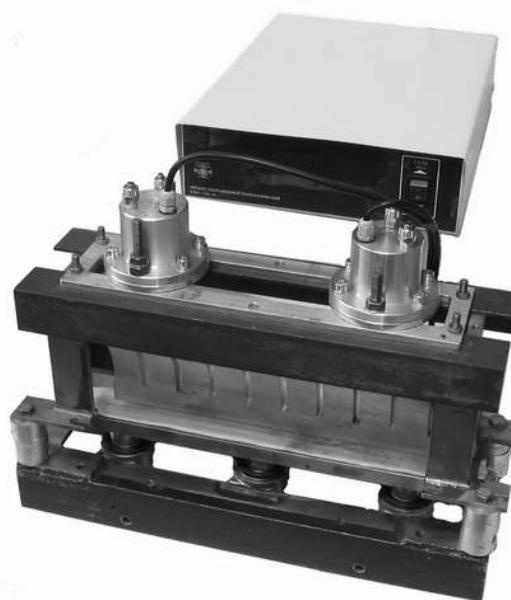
Исследовательский стенд ультразвуковой сварки.
